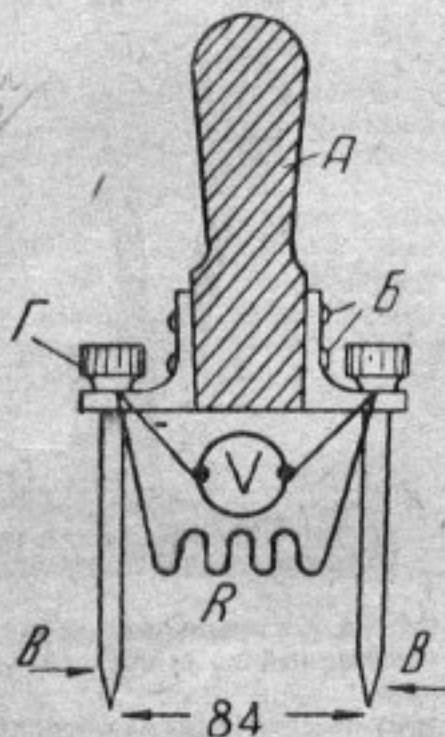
Схема включения приборов на нагрузочной вилке. V—вольтметр т5МШ (3—0—3 вольт); R—сопротивление 0,02 ома — никелин или констан; А—деревянная ручка; Б—крепления—шуруп; В—штыри вилки (изолированы между собой); Г—гайки—крепления сопротивления и вольтметра.
